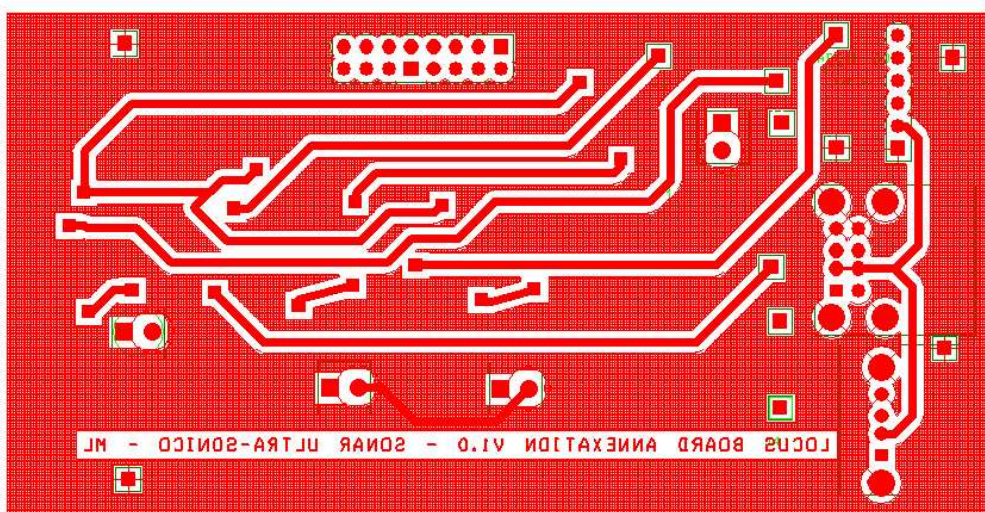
Layout do PCB da extensão à *LocusBoard* - Bottom.
